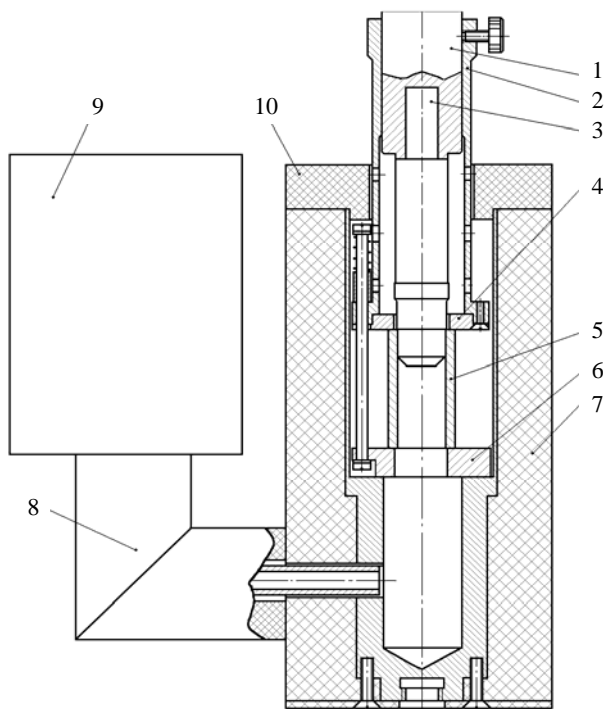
Эскиз приспособления Л429 для дорнования муфт: 1 – толкатель; 2 – корзина; 3 – дорн; 4 – упорный верхний фланец; 5 – муфта; 6 – упорный нижний фланец; 7 – термоизолированный стакан; 8 – термоизолированный патрубок для подачи жидкого азота в рабочую зону; 9 – термоизолированная емкость для жидкого азота; 10 – термоизолирующая крышка
